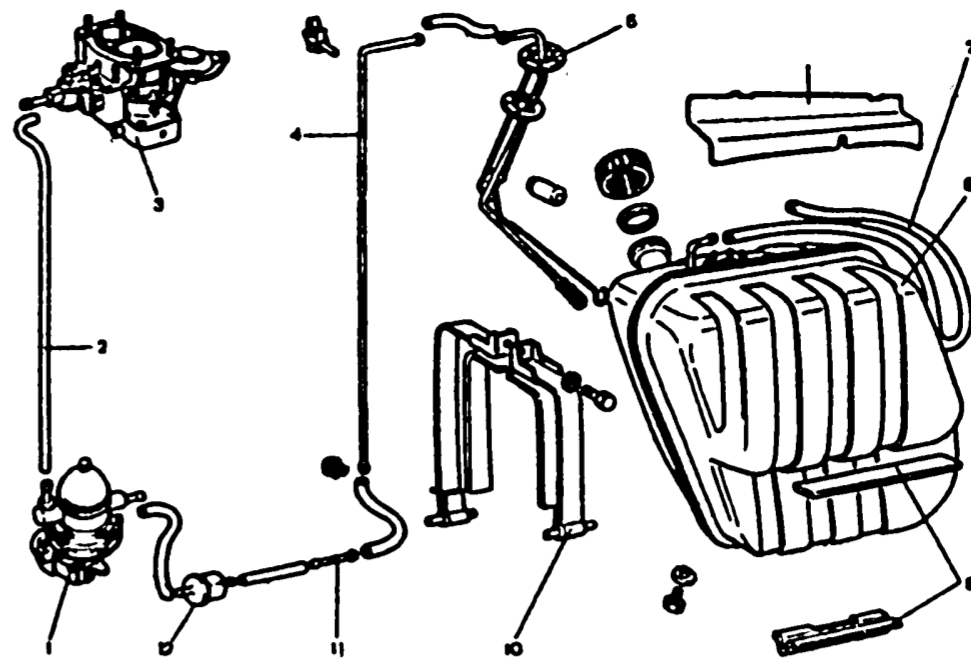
Приборы подачи топлива в карбюратор: 1 - топливный насос; 2 - шланг к карбюратору; 3 - карбюратор; 4 - задняя трубка; 5 - датчик указателя уровня и резерва топлива; 6 - предохранительный щиток; 7 - трубка вентиляции бака; 8 - топливный бак; 9 - прокладки; 10 - хомут крепления топливного бака; 11 - передняя трубка; 12 - фильтр тонкой очистки топлива
